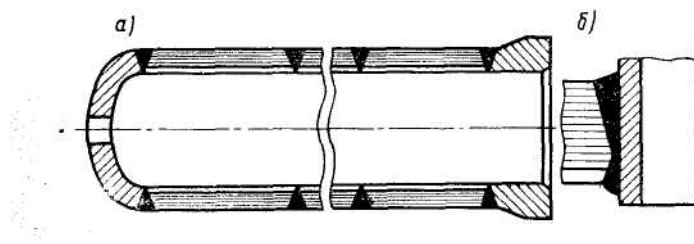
Конструктивне оформлення багат шарової посудини:
